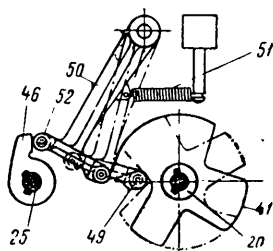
Механическая блокировка между главным и тормозным валами (блокировка ослабления поля):
